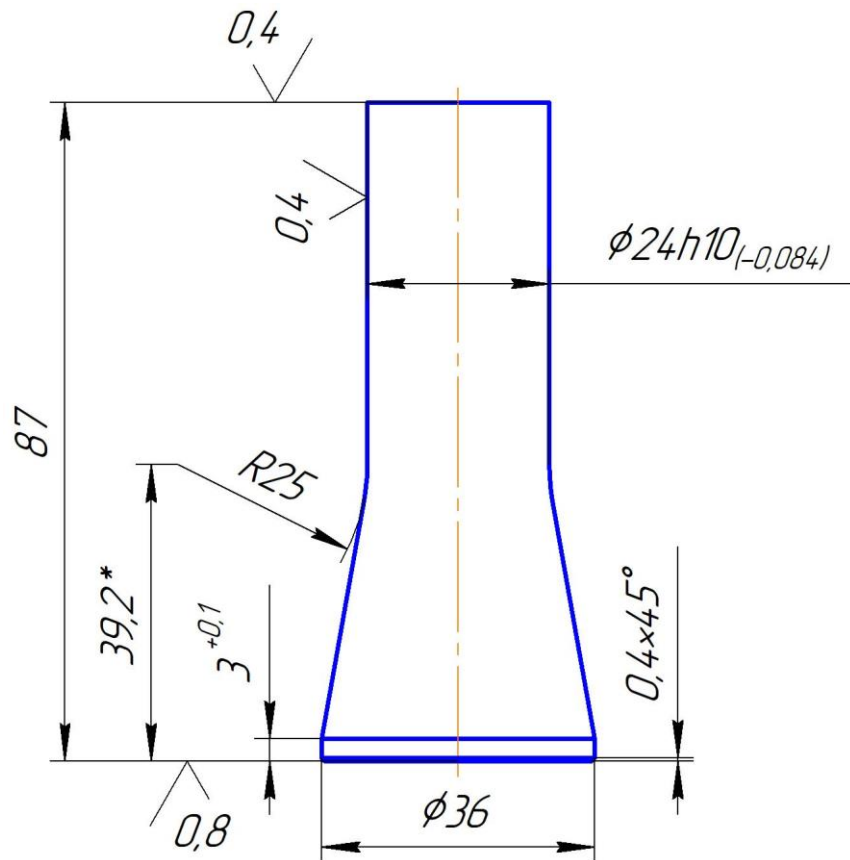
Виштовхувач для зворотного холодного видавлювання деталі «Втулка».
